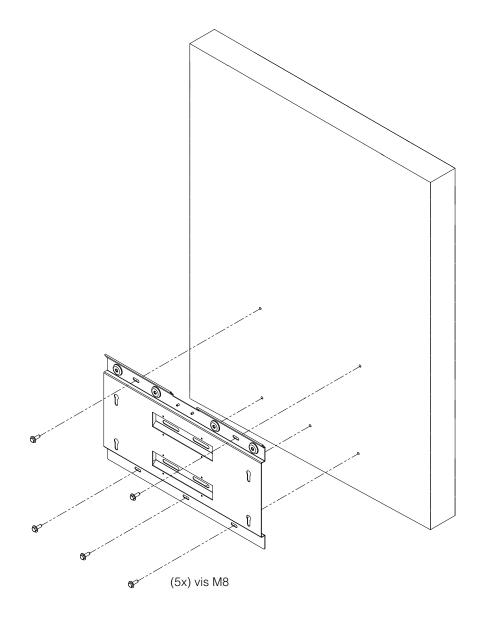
Fixation du support de montage du boîtier de câblage au mur
